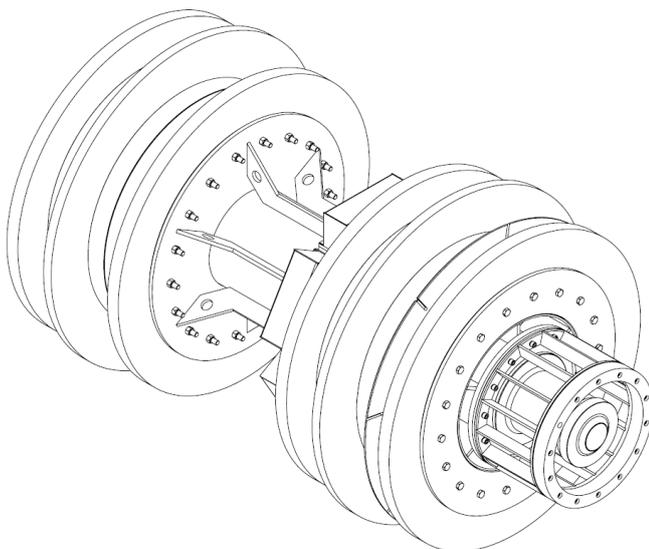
Калибровочный поршень с пластиной для труб диаметром 48 дюймов
